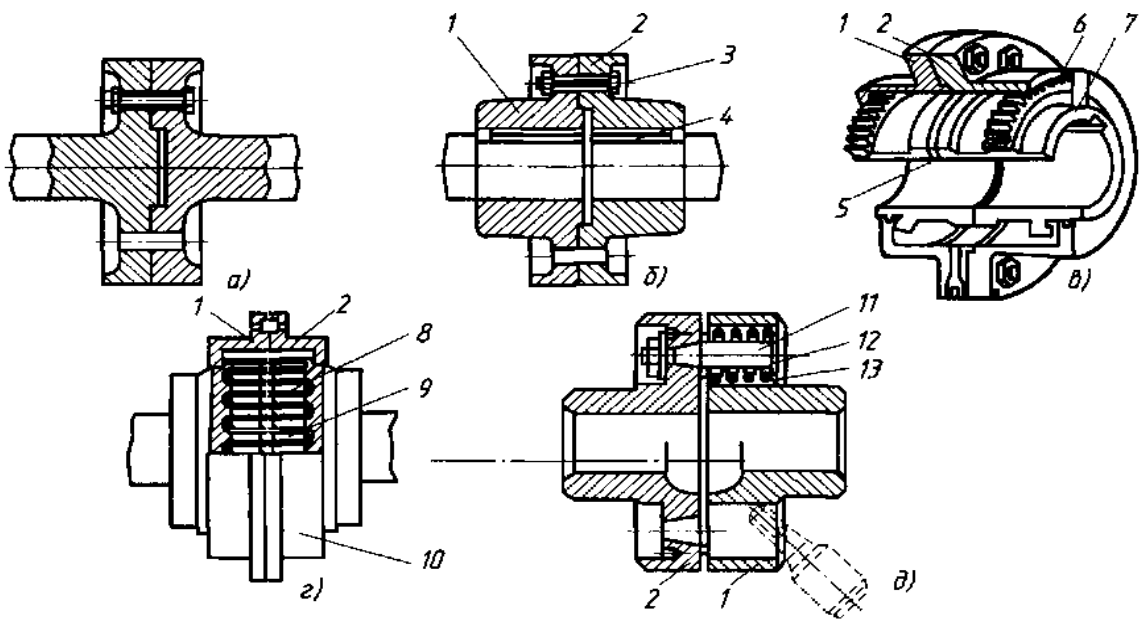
Соединение валов (а) и муфт (б — жесткой поперечно-свертной; в — зубчатой; г — полужесткой зубчато-пружинной; д — упругой втулочно-пальцевой):
